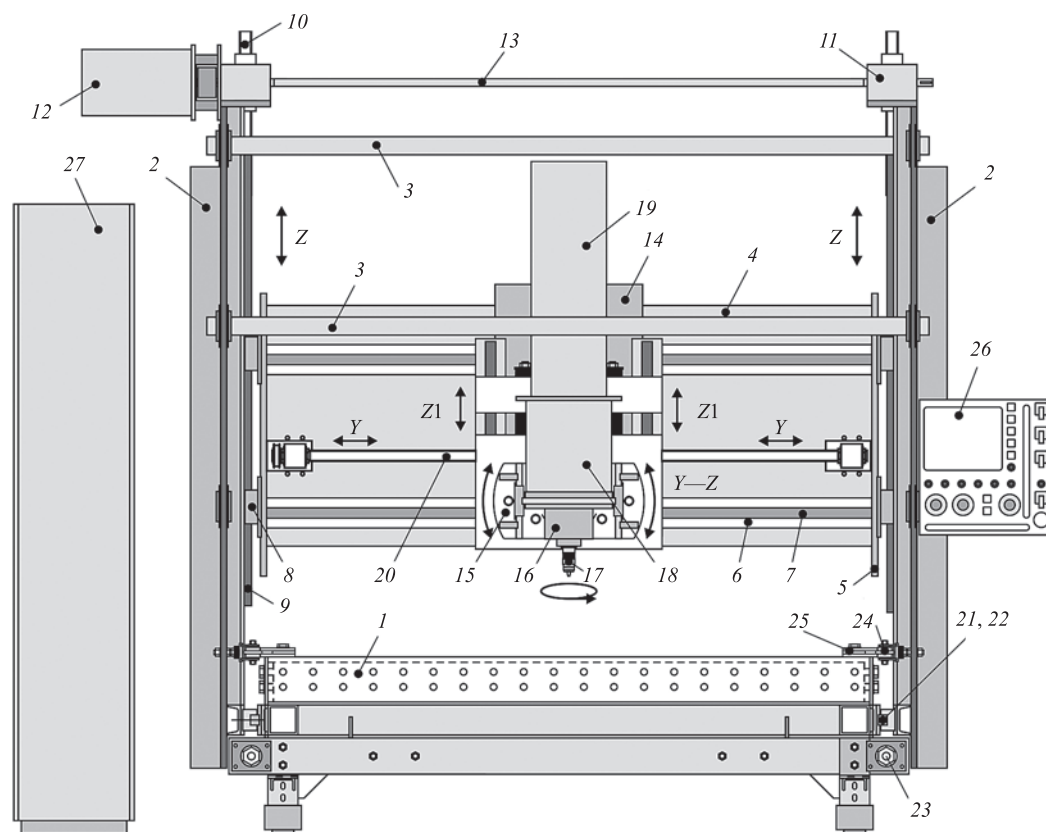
Машина фрикционной сварки "Малахит"
